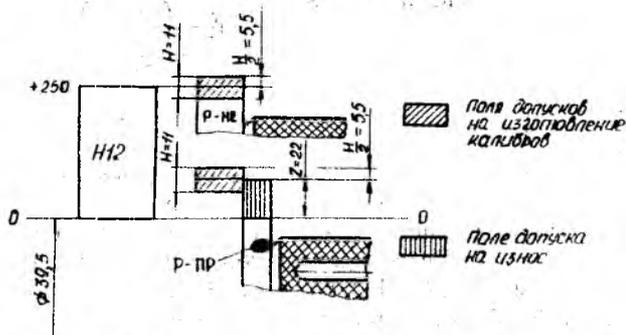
Расположение полей допусков рабочих калибров для контроля отверстия $\varnothing 39,5 H12$
